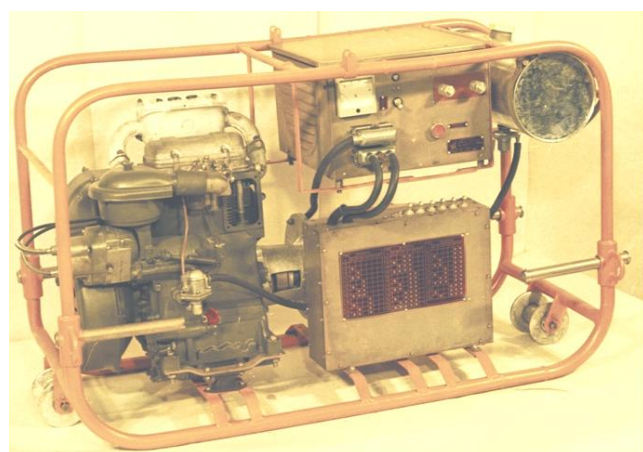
Агрегат сварочный АДБ - 13.02 со ступенчатым регулированием сварочного тока. Внешний вид. Номинальный сварочный ток - 130 А; предел регулирования сварочного тока 20 – 180 А; частота вращения генератора - 6000 мин⁻¹; номинальная мощность генератора - 6,0 кВА; приводной двигатель - УД-25.
